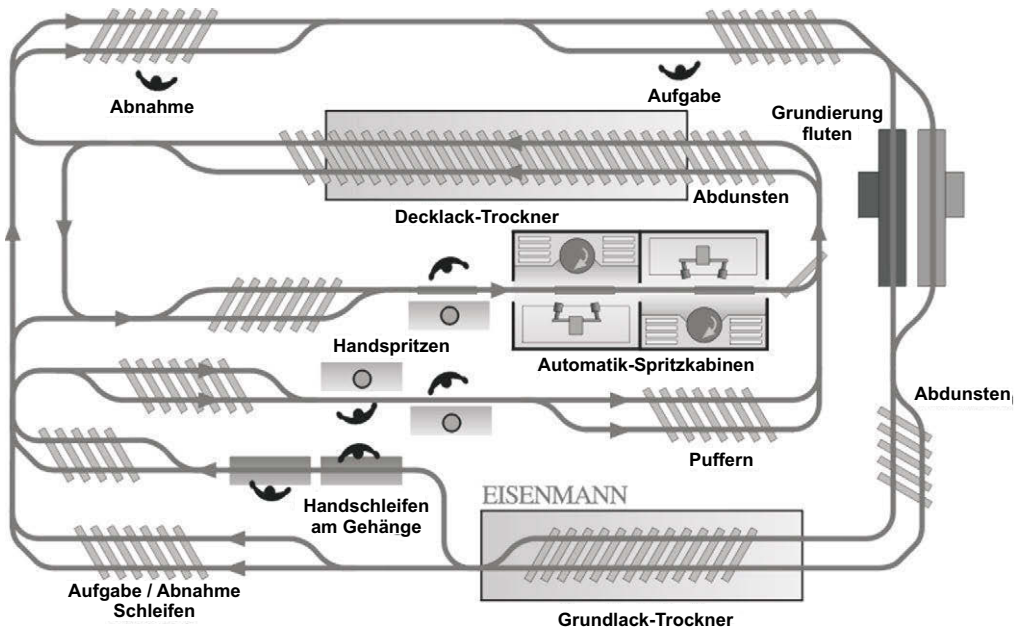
Fahrkurs einer Power-&-Free-Förderanlage für eine Fensterlackierungsstraße
